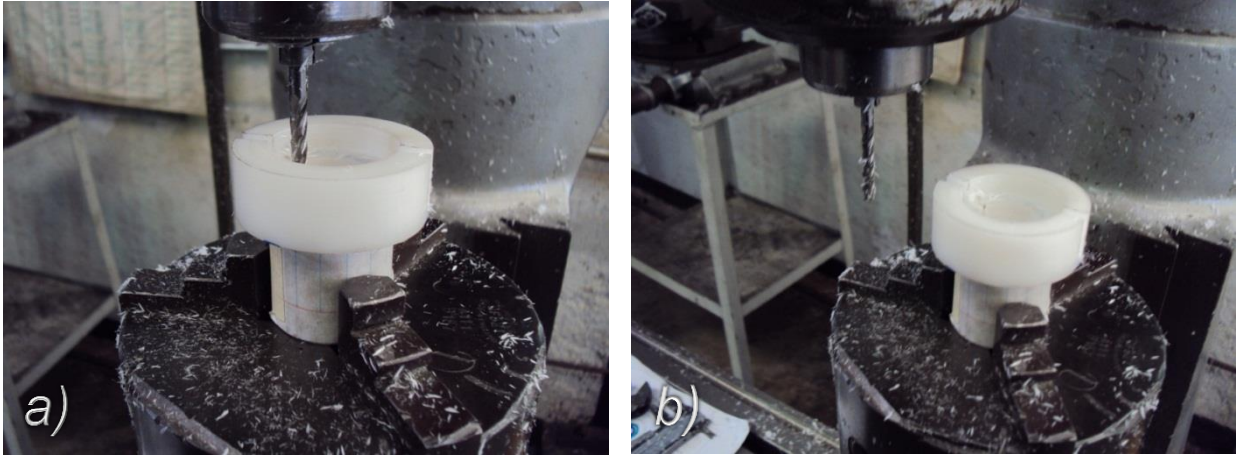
Manufactura de la ranura en la parte hembra del rotor.
